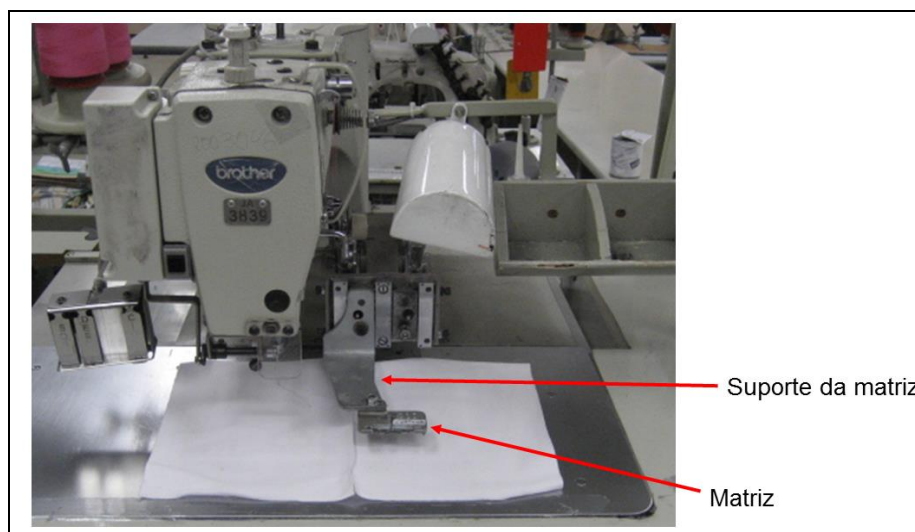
Melhoria da matriz para aplicação de plaquetas
